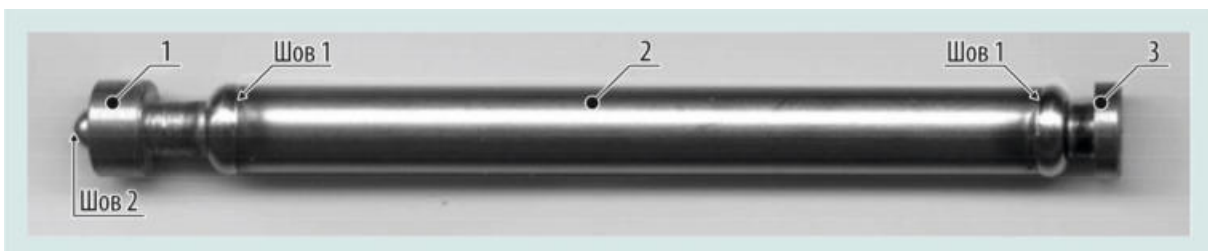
Внешний вид экспериментального газонаполненного образца: 1 — верхняя заглушка; 2 — трубка; 3 — нижняя заглушка
